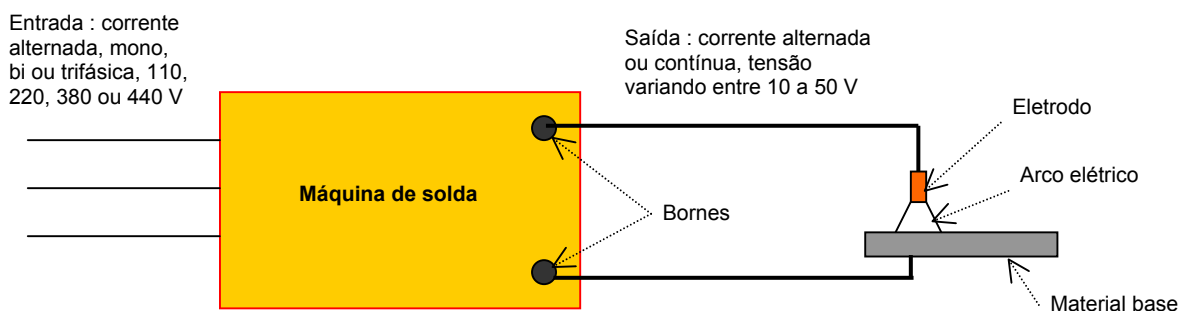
Representação esquemática de uma máquina de solda por arco elétrico.
